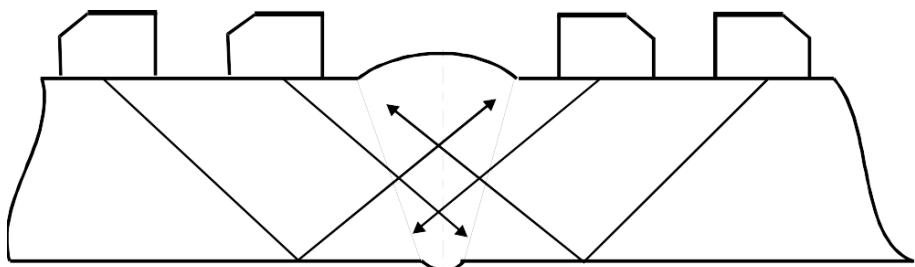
Схемы прозвучивания стыковых сварных соединений на продольные дефекты
